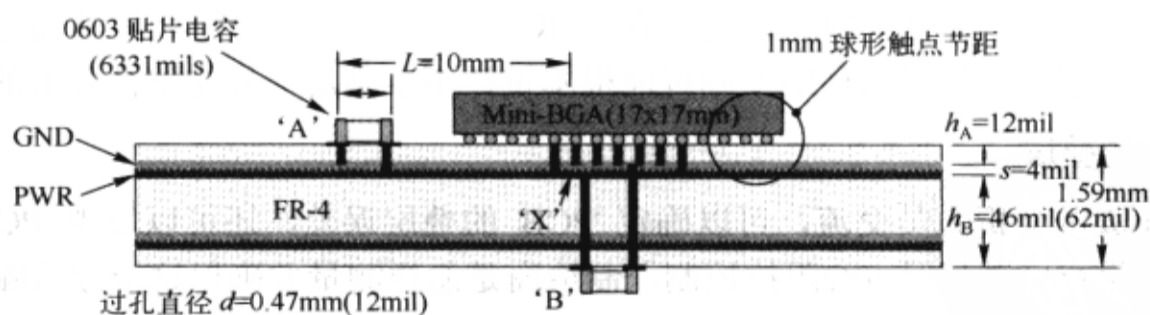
电源/地层存在时 PCB 顶层的电容器
